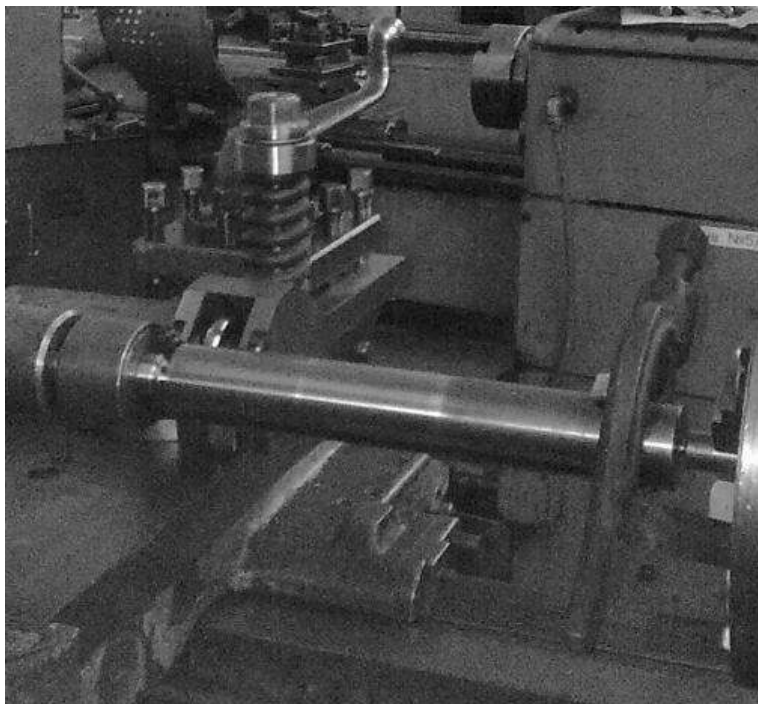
Обкатка вала з роликом на верстаті 1К62
